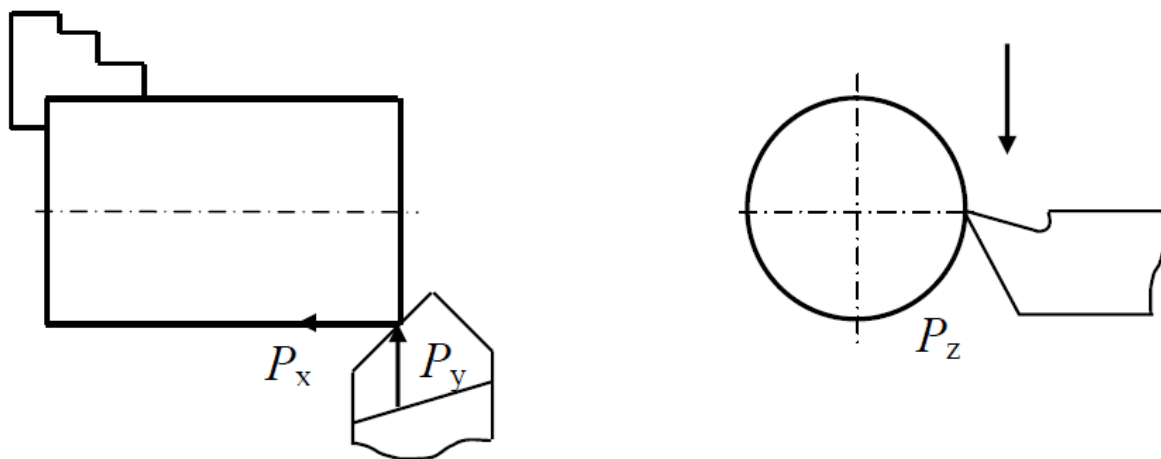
Схемы сил резания, действующих при обработке вала на токарном станке
